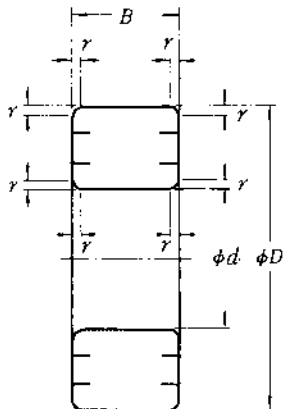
Габаритные размеры радиальных шарикоподшипников и роликоподшипников
